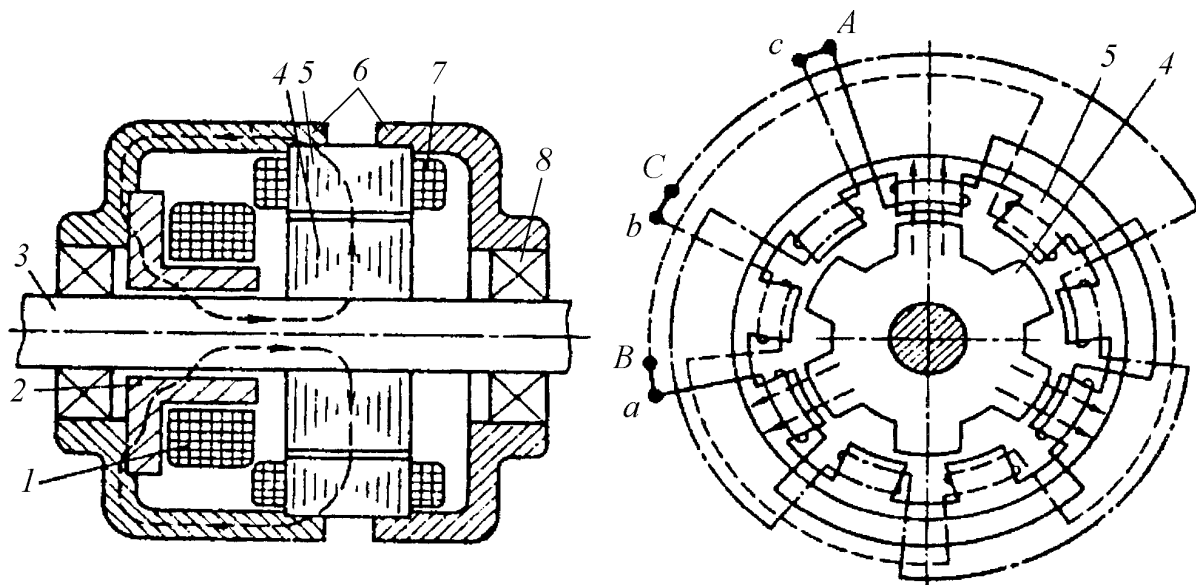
Конструктивная схема генератора индукторного типа:
